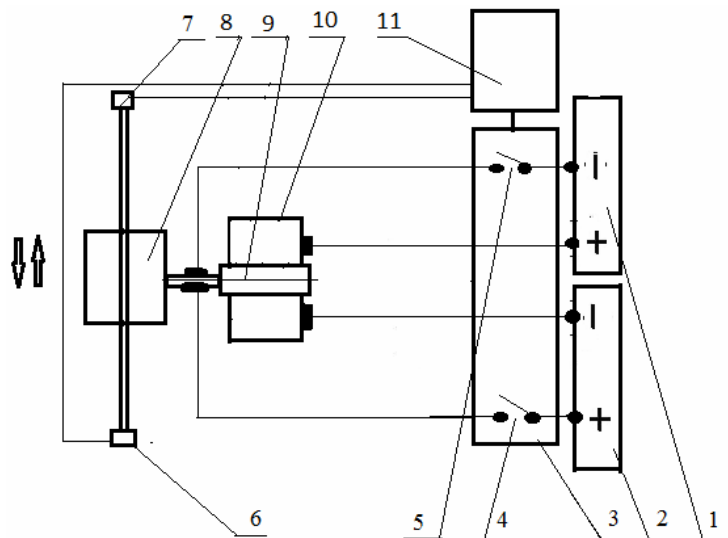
Схема устройства: 1, 2 – источники постоянного тока; 3 – блок коммутации токов; 4, 5 – реле; 6, 7 – концевые датчики; 8 – привод линейного перемещения шлифовального инструмента; 9 – шлифовальный инструмент; 10 – обрабатываемая деталь; 11 – блок управления коммутацией токов
